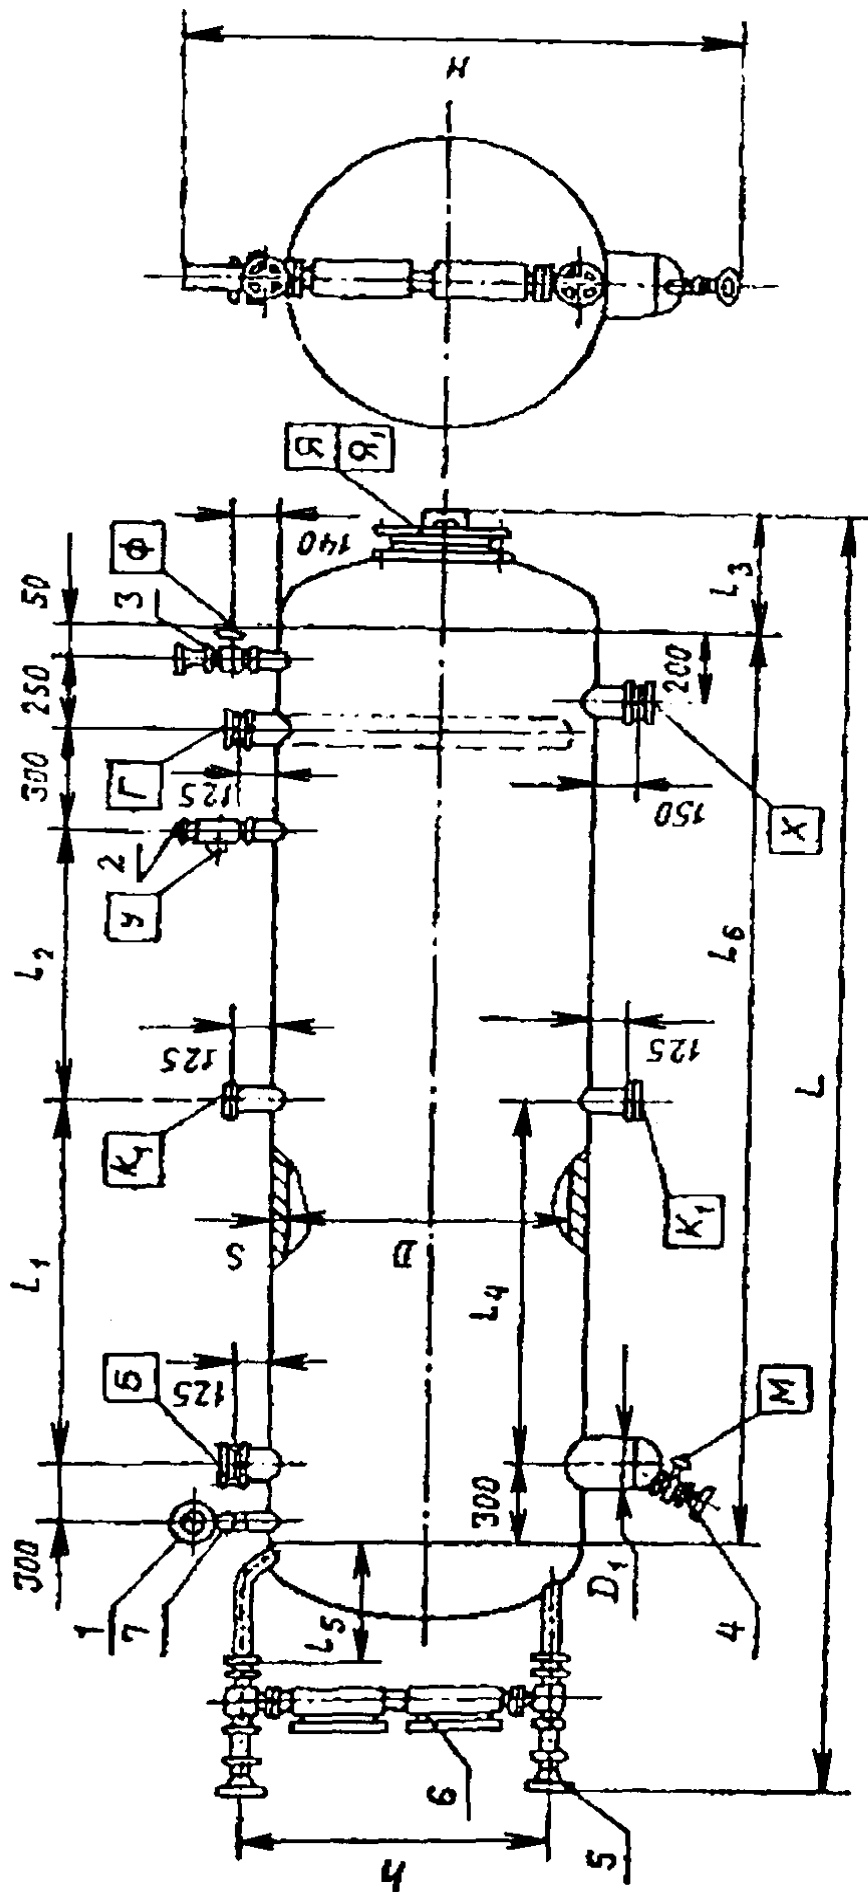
Общий вид дренажного ресивера типа РД
